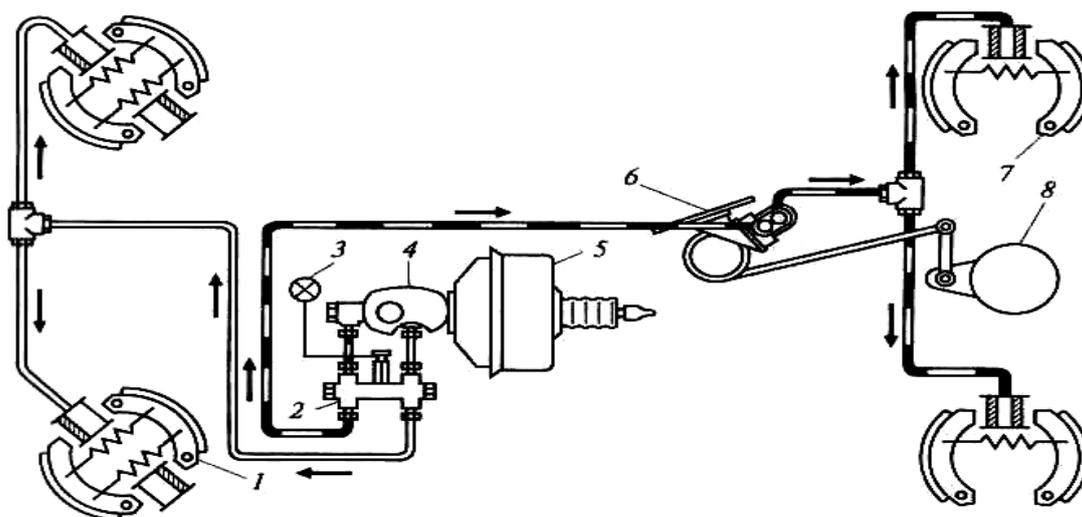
Двухконтурная схема рабочей тормозной системы автомобиля ГАЗ-31029 «Волга»: 1-передний тормозной механизм; 2 — сигнальное устройство; 3 — сигнализатор неисправности рабочих тормозов; 4 — главный тормозной цилиндр; 5 — вакуумный усилитель; 6 — регулятор давления; 7 — задний тормозной механизм; 8 — кожух полуоси заднего моста с кронштейном
